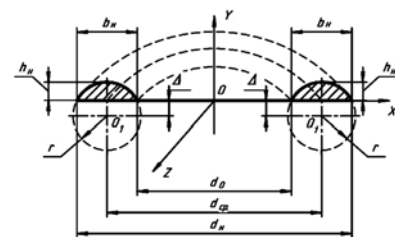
Схематичное представление диаметрального сечения напльвов металла и форма образуемой ими поверхности по краю лунки
